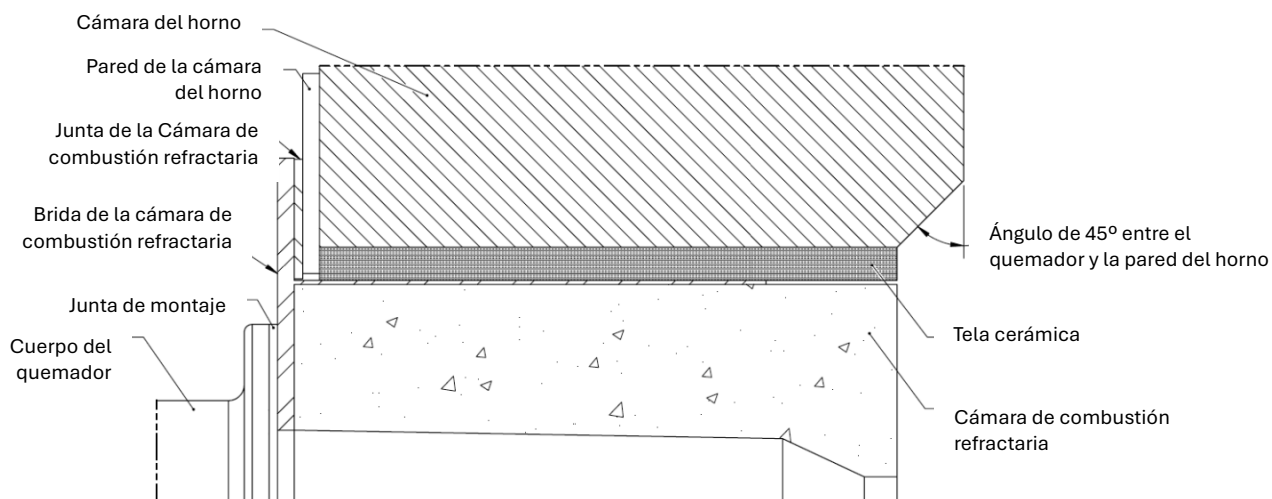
Cámara de combustión de carburo de silicio montada en la cámara del horno
